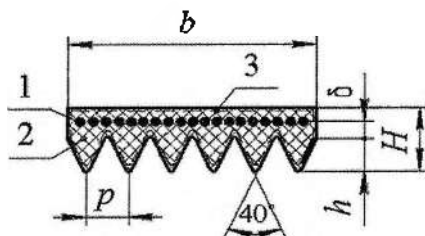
Конструкция и размеры поперечного сечения поликлинового ремня
